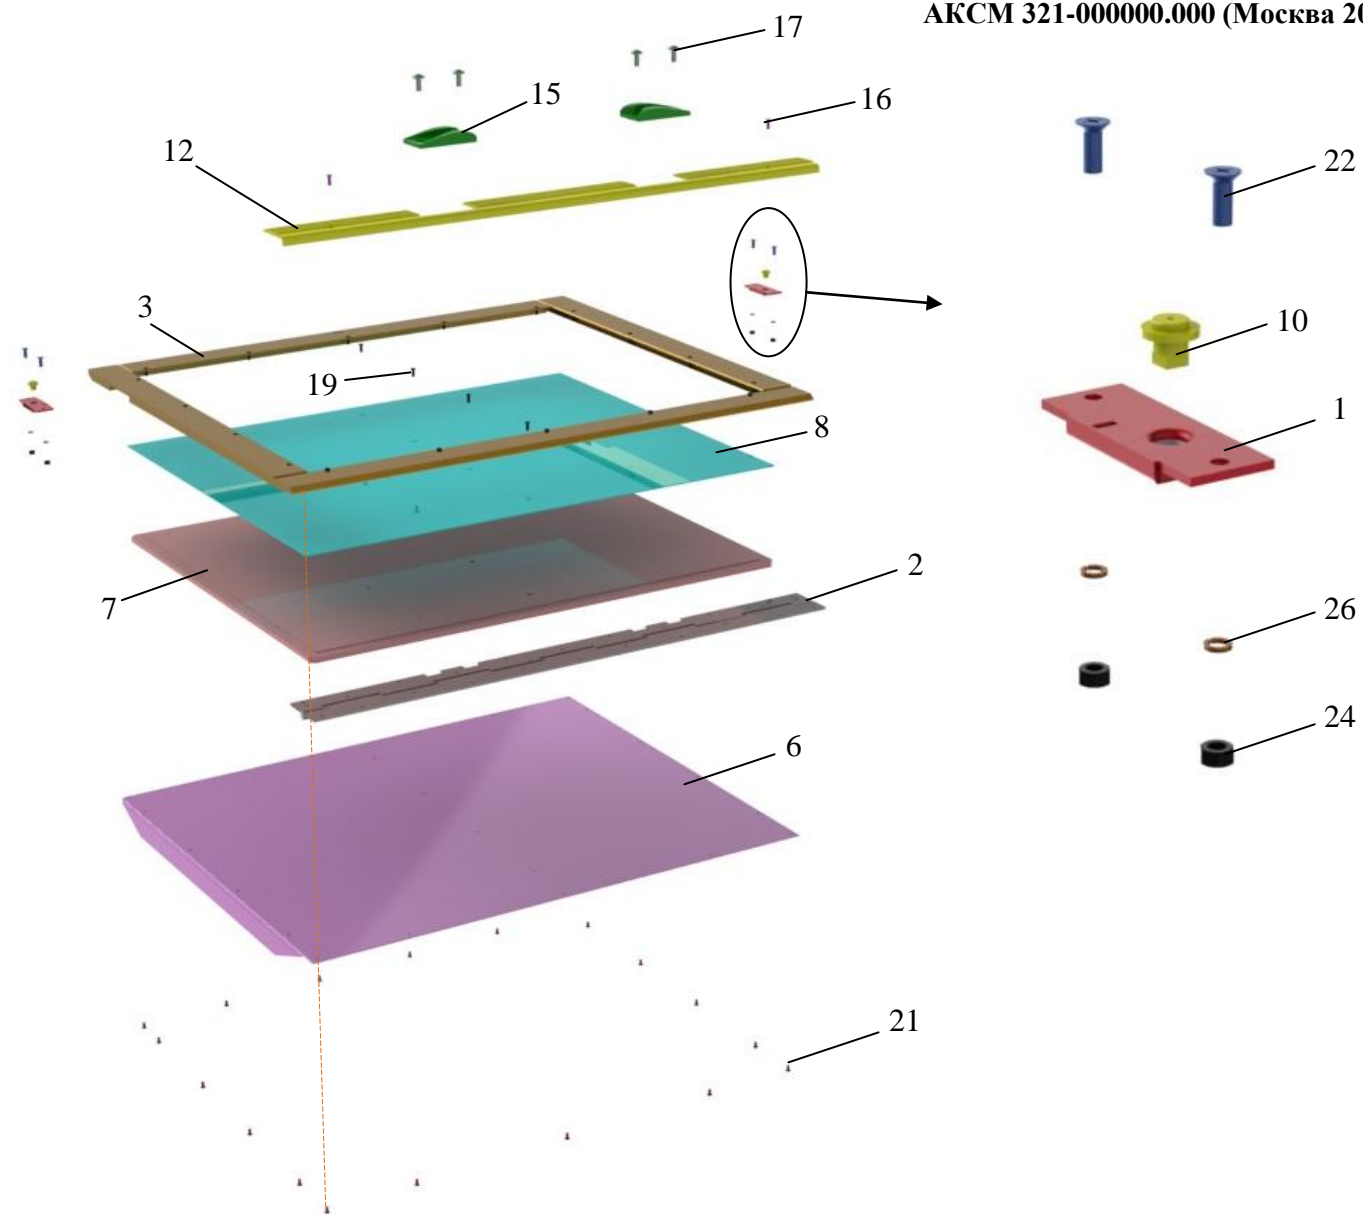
Аппарель АКСМ 321-132804.000
